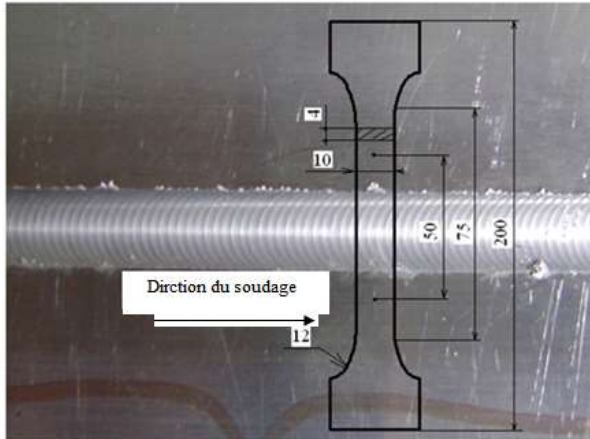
Découpage d'éprouvettes dans des tôles soudées par FSW
